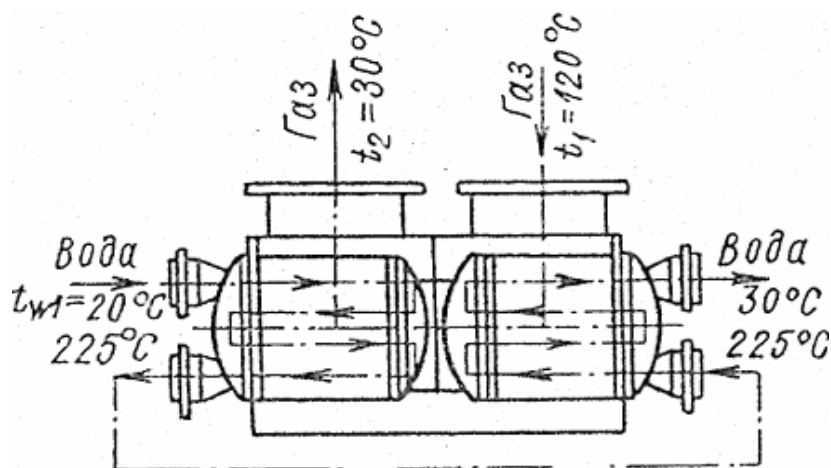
Схема промежуточного газоохладителя промышленного центробежного компрессора — два последовательно обтекаемых газом трубных пучка в общем корпусе.
